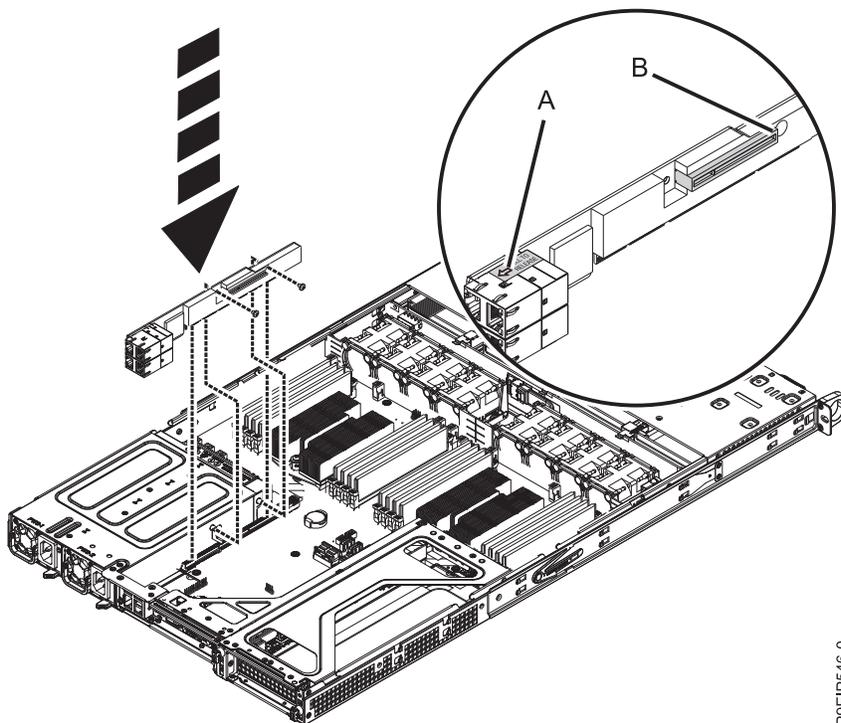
Cómo volver a poner los tornillos de la tarjeta de expansión PCIe
